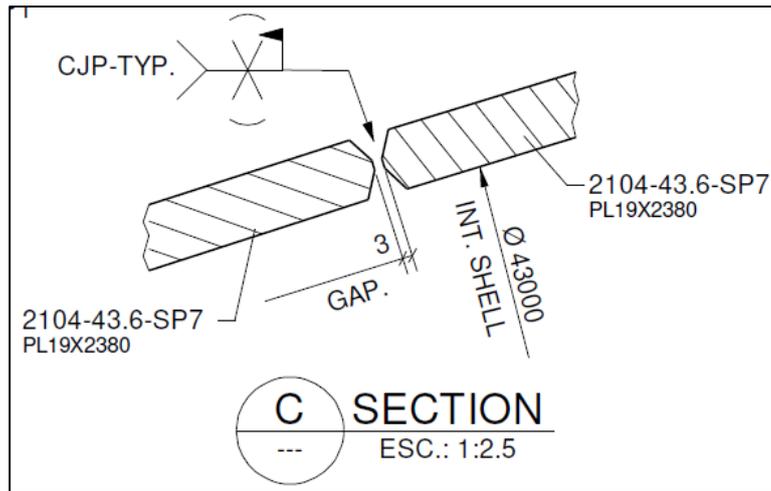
Detalle de soldadura Vertical de Anillos de Casco
